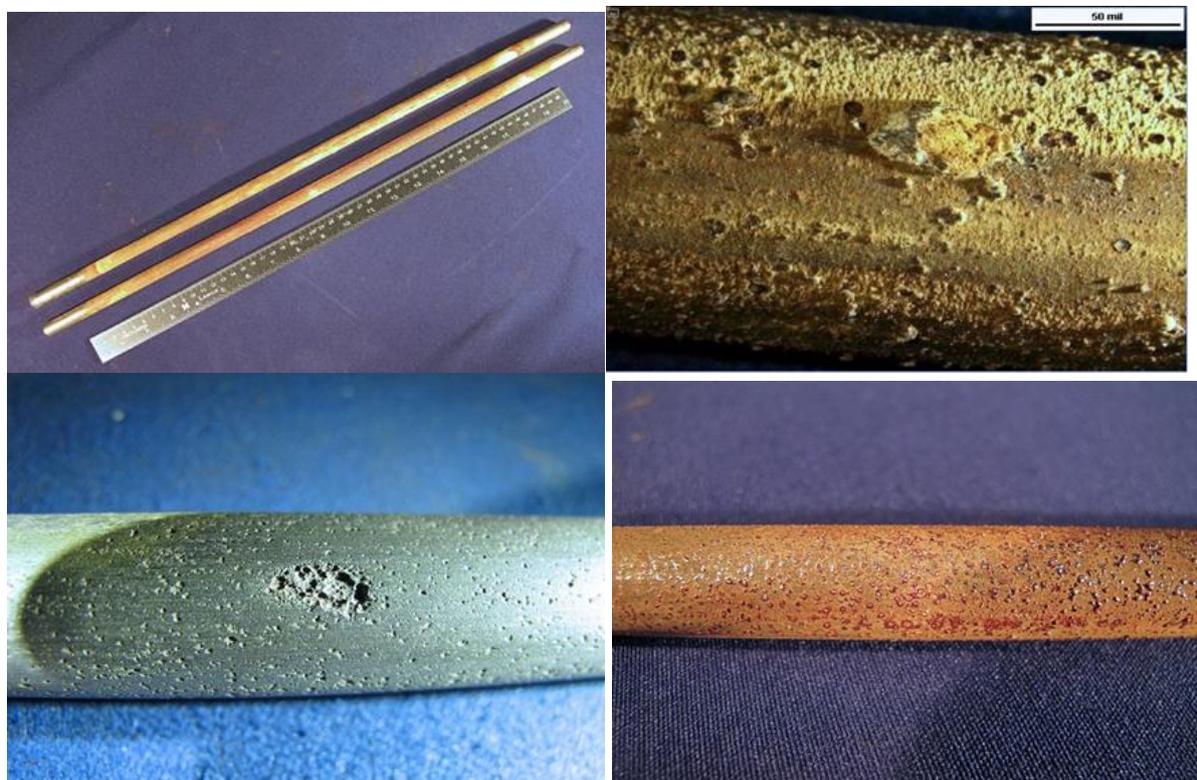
Detalhe visual dos tubos-teste no Sentinel: problemas de corrosão e incrustação (taxa de corrosão de 30 mills, pitting)
